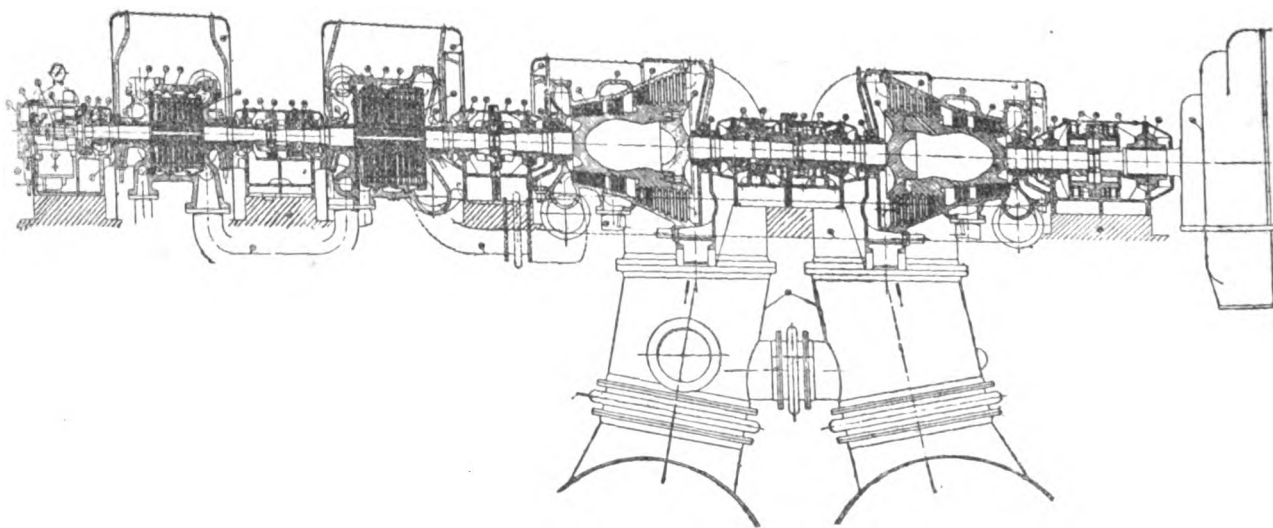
Coupe transversale de la turbine Stork E-B. de 16000 kw de l'usine « Merwede-Kanaal », à Utrecht.
